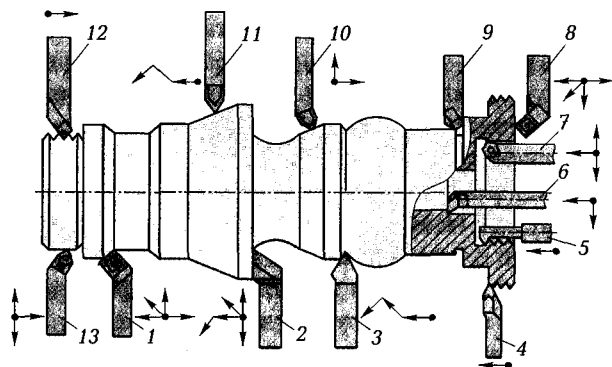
Виды резцов, применяемых на токарных станках с ЧПУ:
